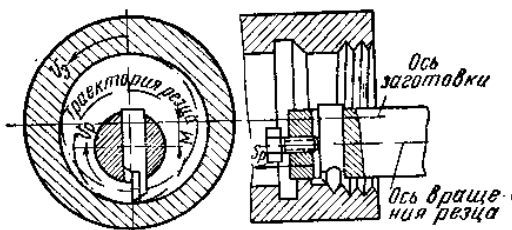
Схема вихревого фрезерования внутренней резьбы
